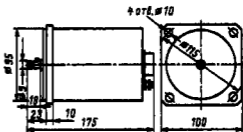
33 Габаритные и установочные размеры двигателя ДБ100-60-1,5
